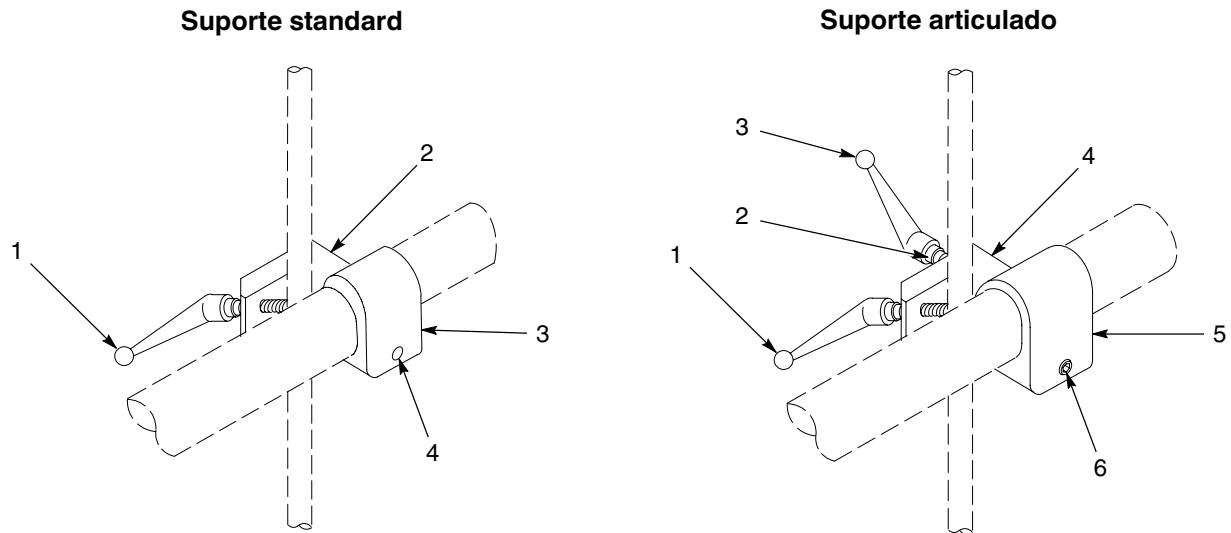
Suportes de barra de pistola para pistolas com tubo de suporte
